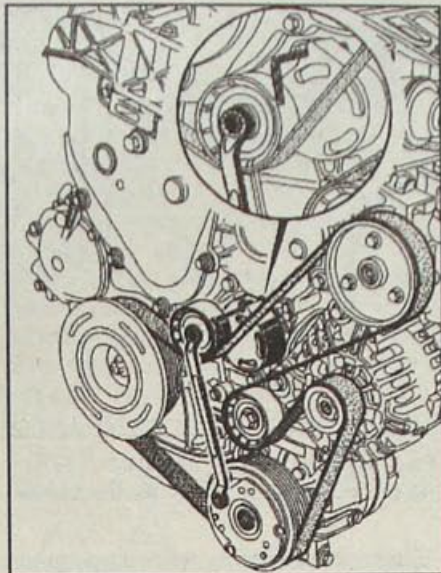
Ослабление натяжения ремня привода вспомогательного оборудования
